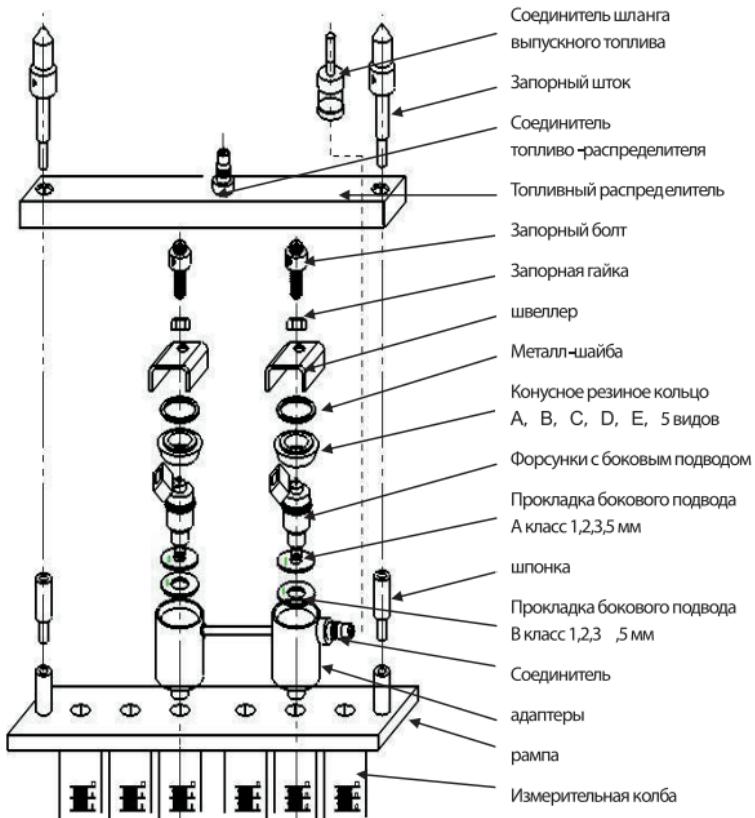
Общий монтаж форсунки с боковым подводом топлива
